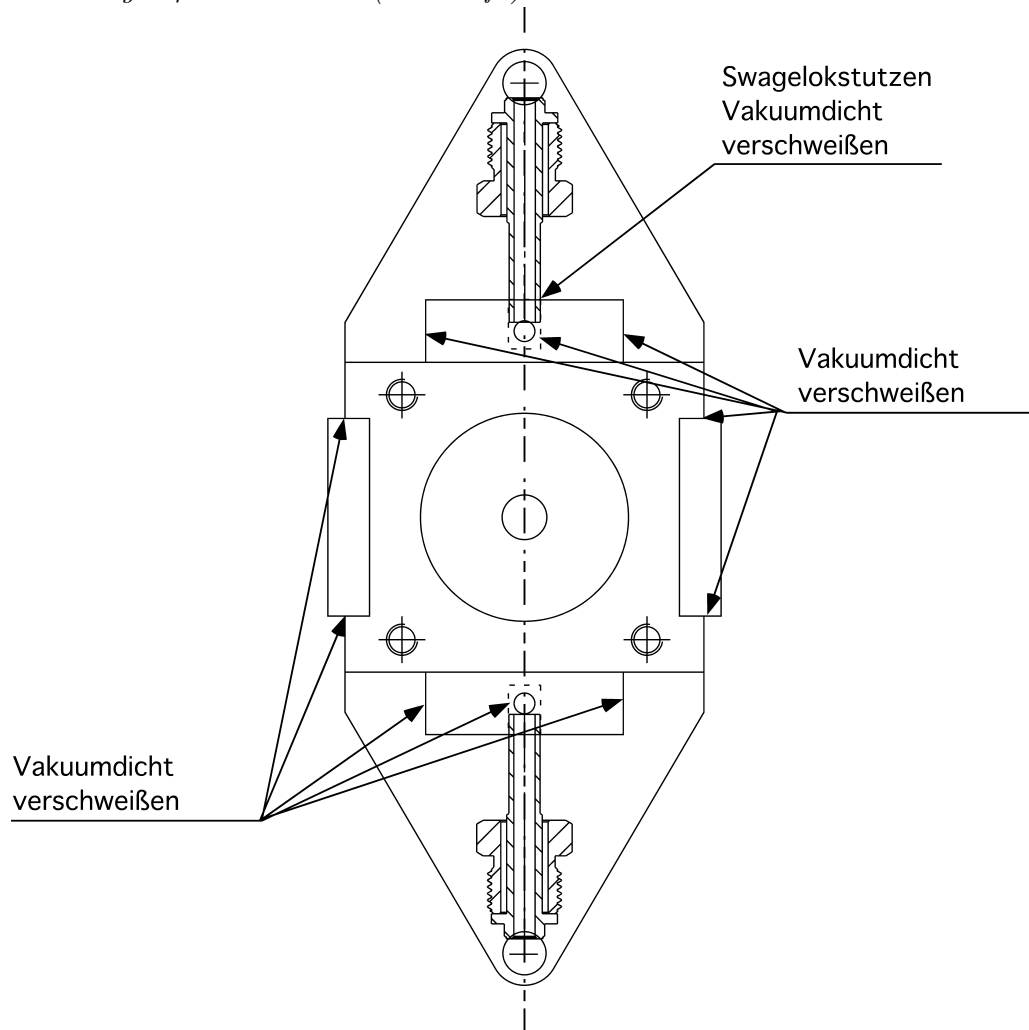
Hier sind die letzten Schweißarbeiten gezeigt, durch die der Schrittmotorhalter sowohl Vakuumtauglich als auch wassergekühlt wurde.
